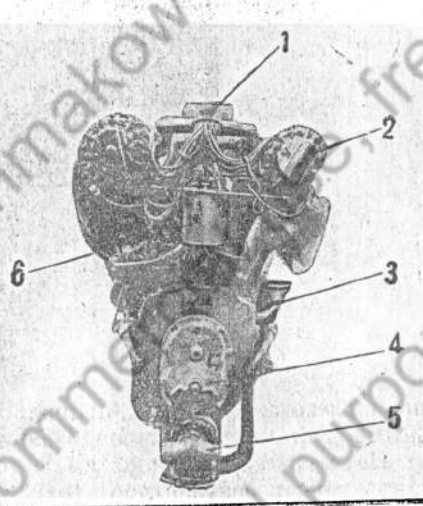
Вид двигателя со стороны заводной рукоятки.
